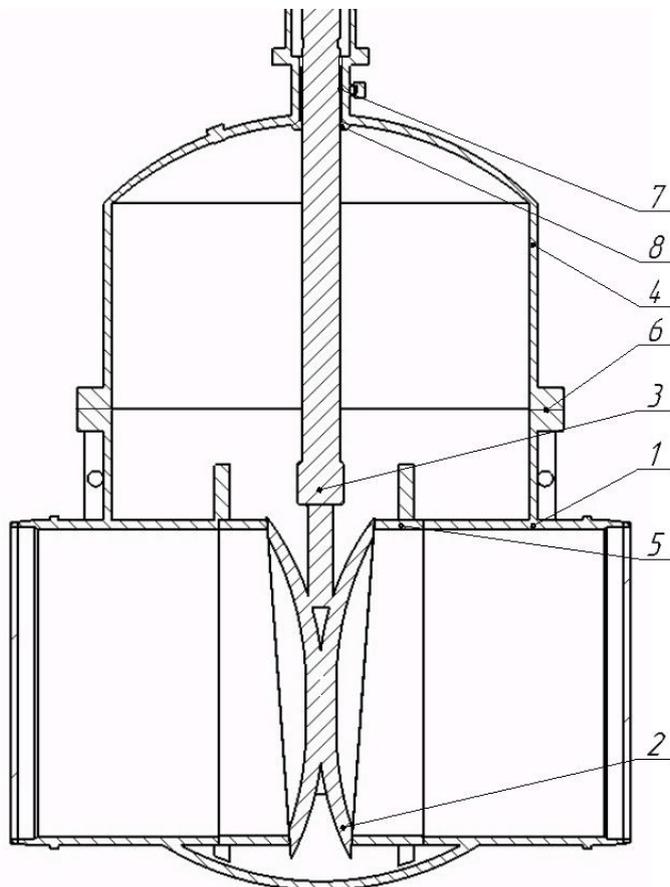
Схема клиновой задвижки 30с905нж
